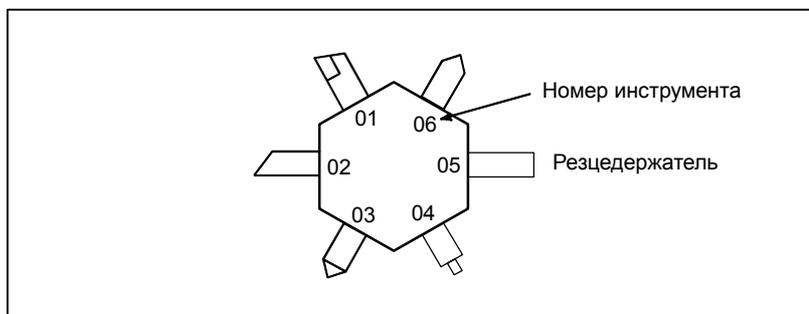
(b) Инструмент, используемый для различных видов обработки
